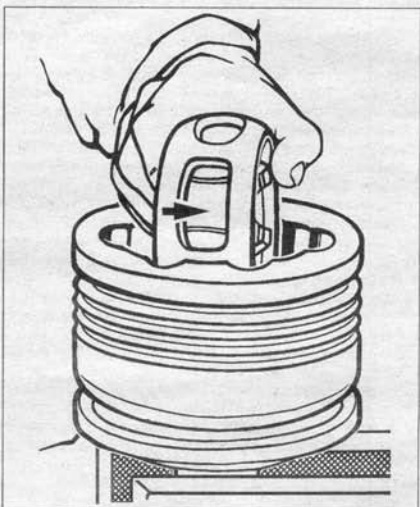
Извлечение сепаратора в сборе с обоймой из корпуса шарнира
